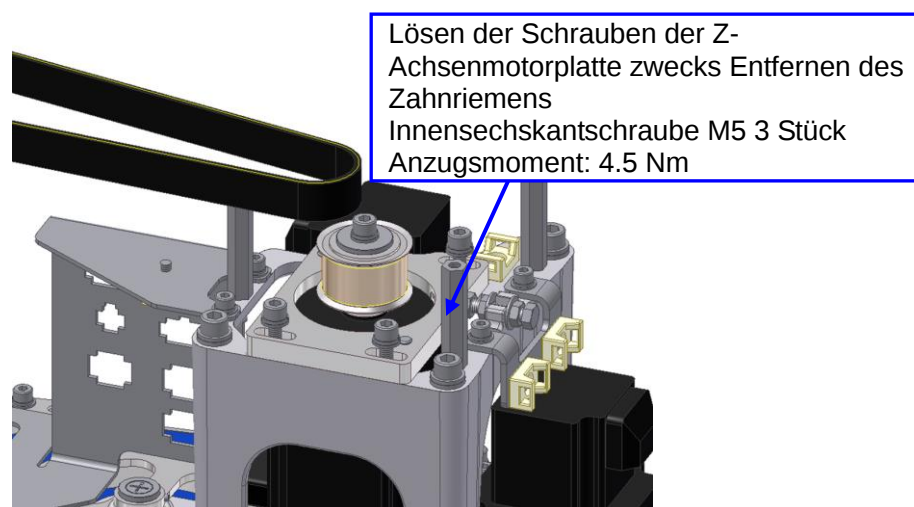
Entfernen des Z-Achsen-Zahnriemens
